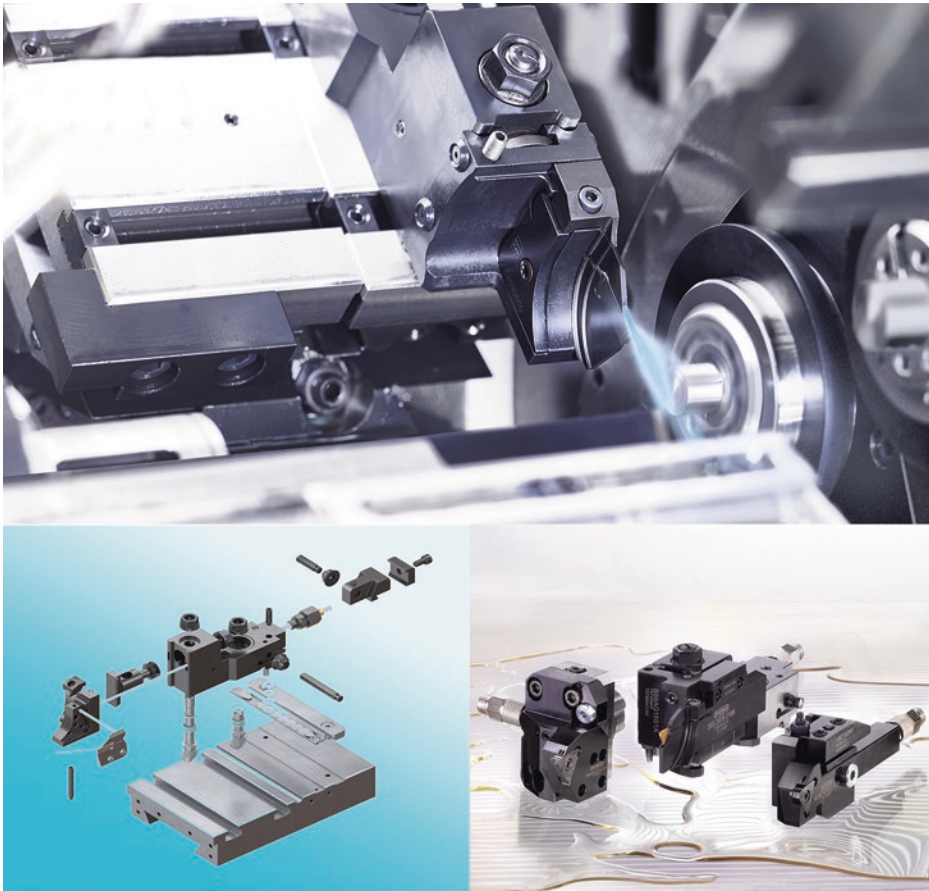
Werkzeugsystem für Schütte-Kurvenmaschine mit innerer Kühlschmiermittelzufuhr und verschiedenen Werkzeughaltern. [Quelle: Schütte]
